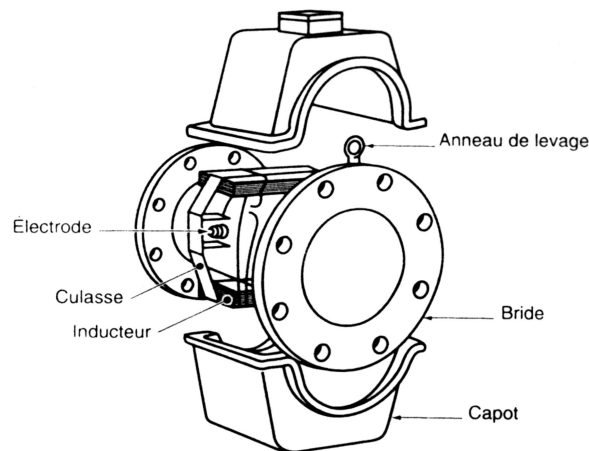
Vue éclatée d'un débitmètre à champ uniforme constant; montage à bride
